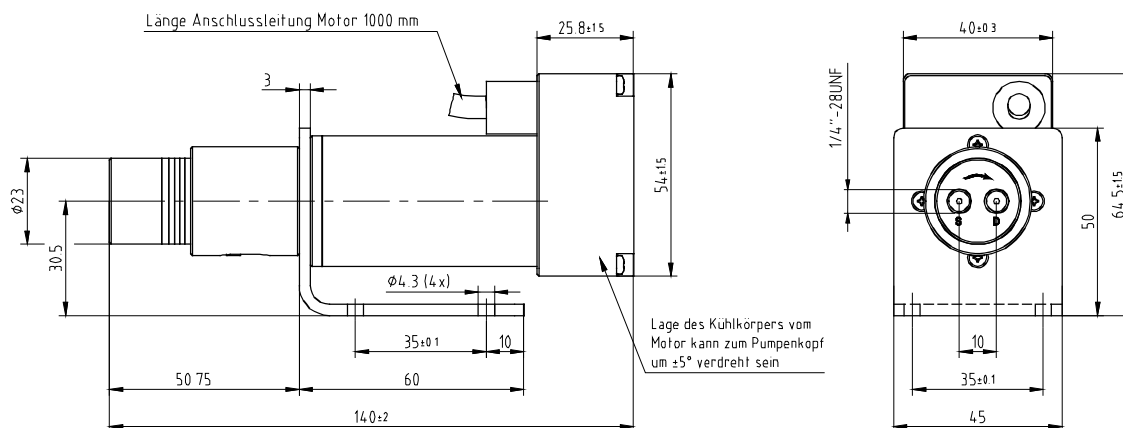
Abmessungen Mikrozahlringpumpe m zr-2905
